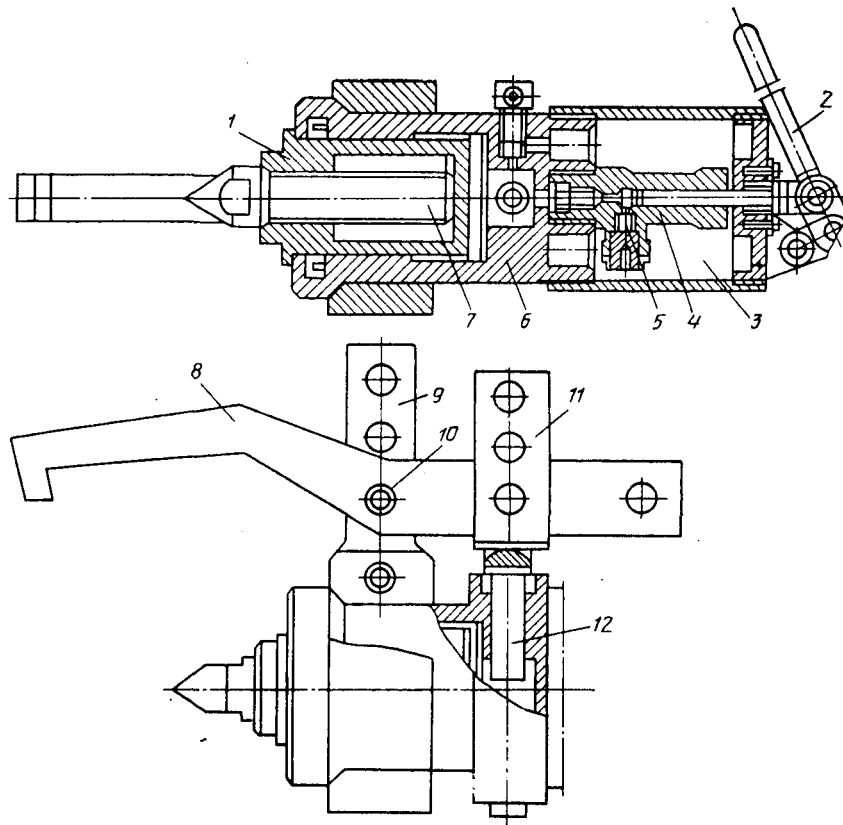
Переносний гідравлічний прес – знімач: 1 – відцентровий плунжер; 2 – рукоятка; 3 – масляний резервуар; 4 – ручний плунжерний насос; 5 – перепускний клапан; 6 – корпус; 7 – висувний упорний гвинт; 8 – лапа; 9 – знімаюча траверса; 10 – болт; 11 – скоба.
